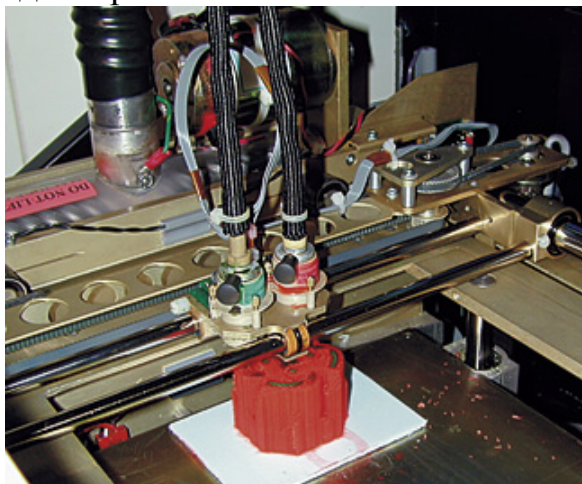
Внешний вид печатающей каретки 3D принтера
